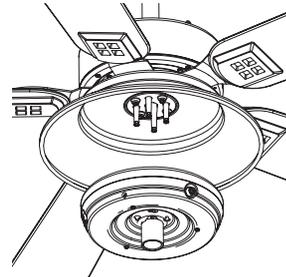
Forma de instalar la parte inferior de la caja del interruptor con el conjunto de luces.
